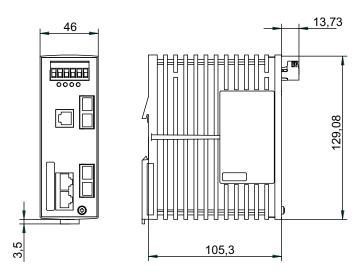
dimensiones de las variantes de dispositivo RS20-04...B
